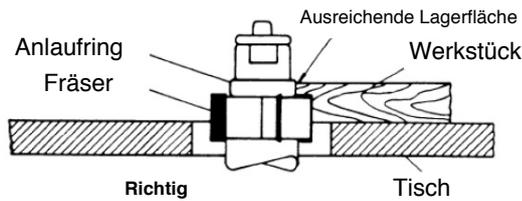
Fräsen mit Anlaufring mit ausreichende Anlaufläche
